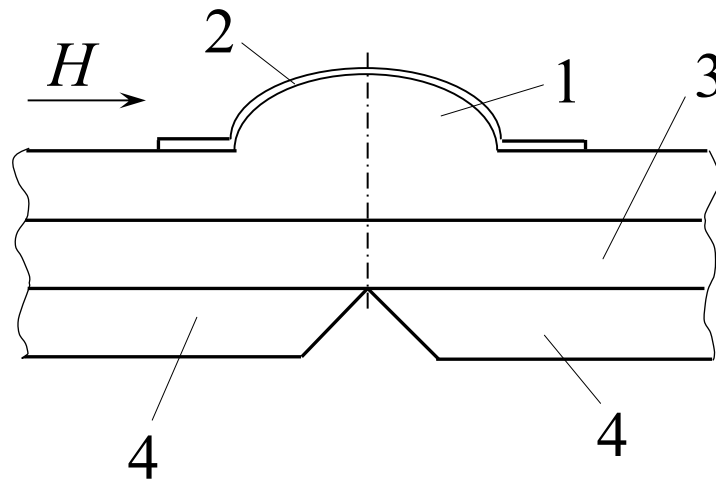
Вид и расположение КМИ при осуществлении способа намагничивания [3]: 1 – контролируемый сварной шов; 2 – магнитная лента; 3 – промежуточная пластина; 4 – пластины со скосом кромок
